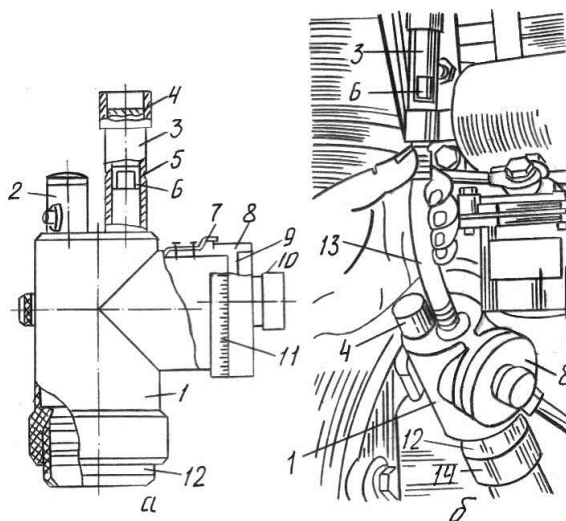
Индикатор расхода газов КИ-13671-ГОСНИТИ: а) конструкция; б) установка на дизель Д-240: 1 – корпус; 2 – пробка; 3 – сигнализатор; 4 – колпачок; 5 – риска; 6 – поплавок; 8 – крышка; 9 – щель; 10 – пружинный фиксатор; 11 – шкала; 12 – переходник; 13 – наставка; 14 – маслозаливная горловина дизеля
